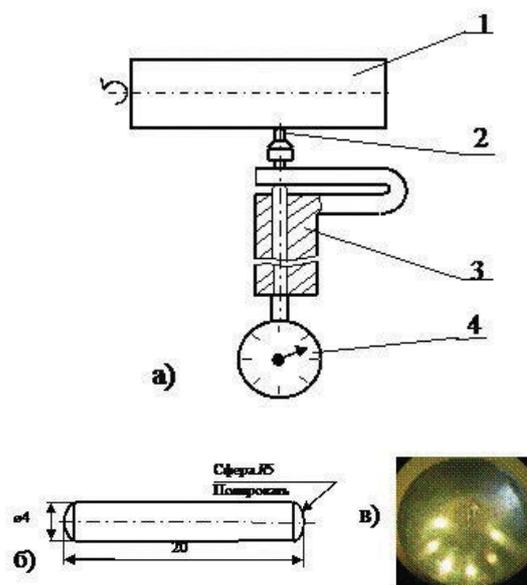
Устройство для предварительного исследования экранирующих свойств технологических смазок: а) схема устройства; б) деформирующий инструмент; в) налип обработанного металла на рабочей поверхности инструмента, х 32
